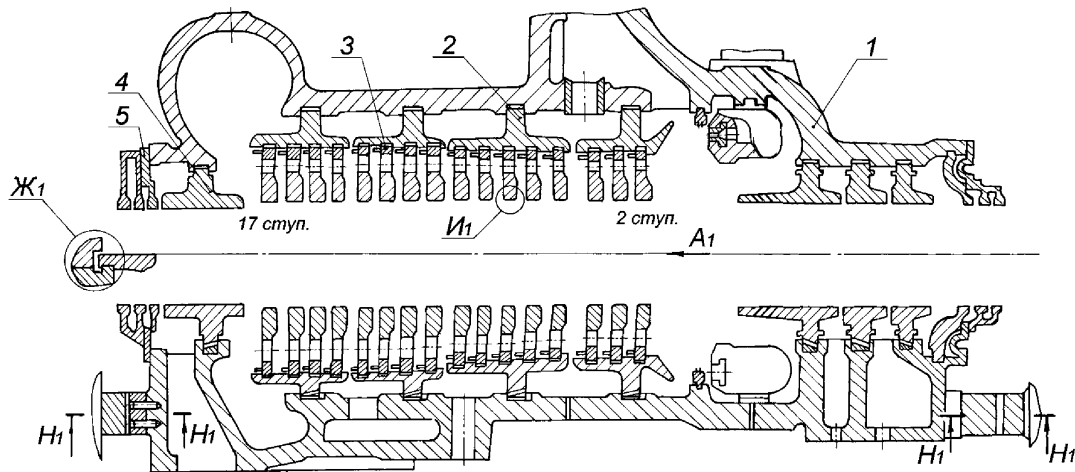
, лист 1 – Корпусные части цилиндра ВД
